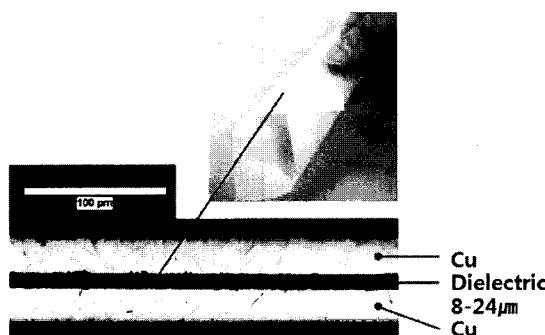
Oak-Mitsui社의 소재가 적용된 PCB 부품.
